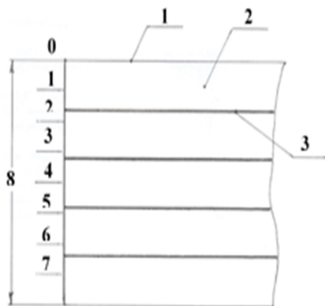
Схема пакета печатных плат из 5 пластин.
